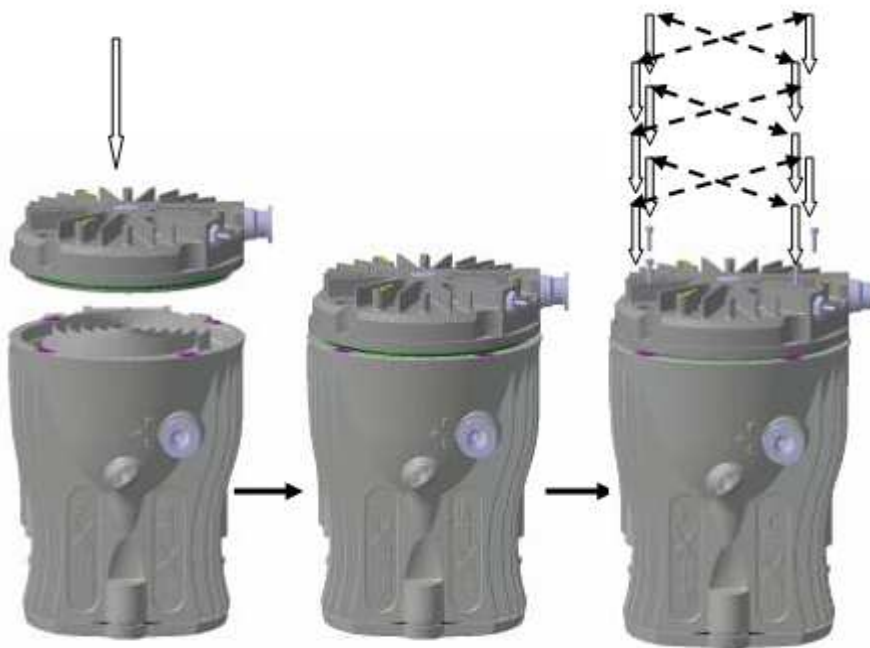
Montáž statoru a následně rotoru do tělesa vývěvy
